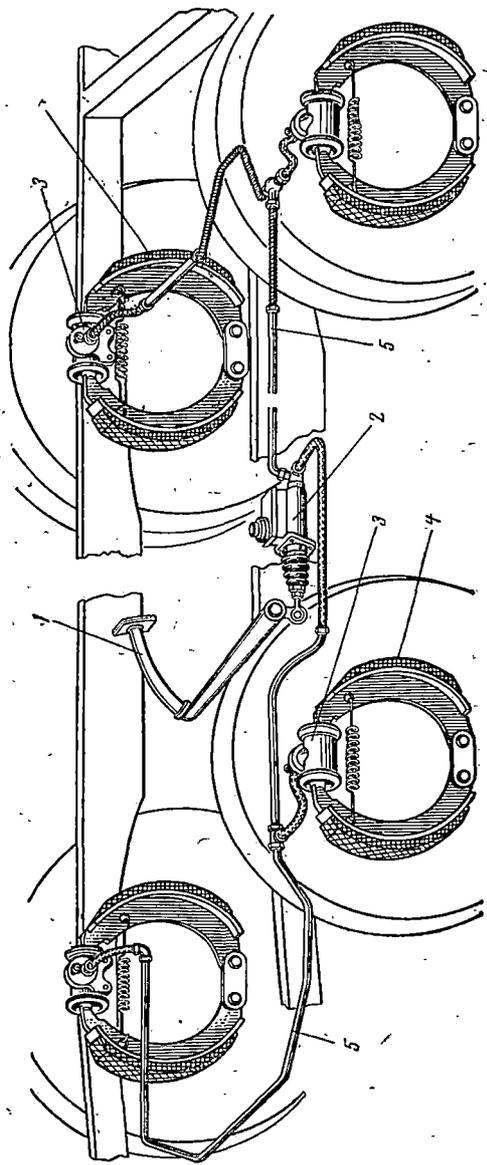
Схема ножного тормоза автомобиля ГАЗ-51А:
